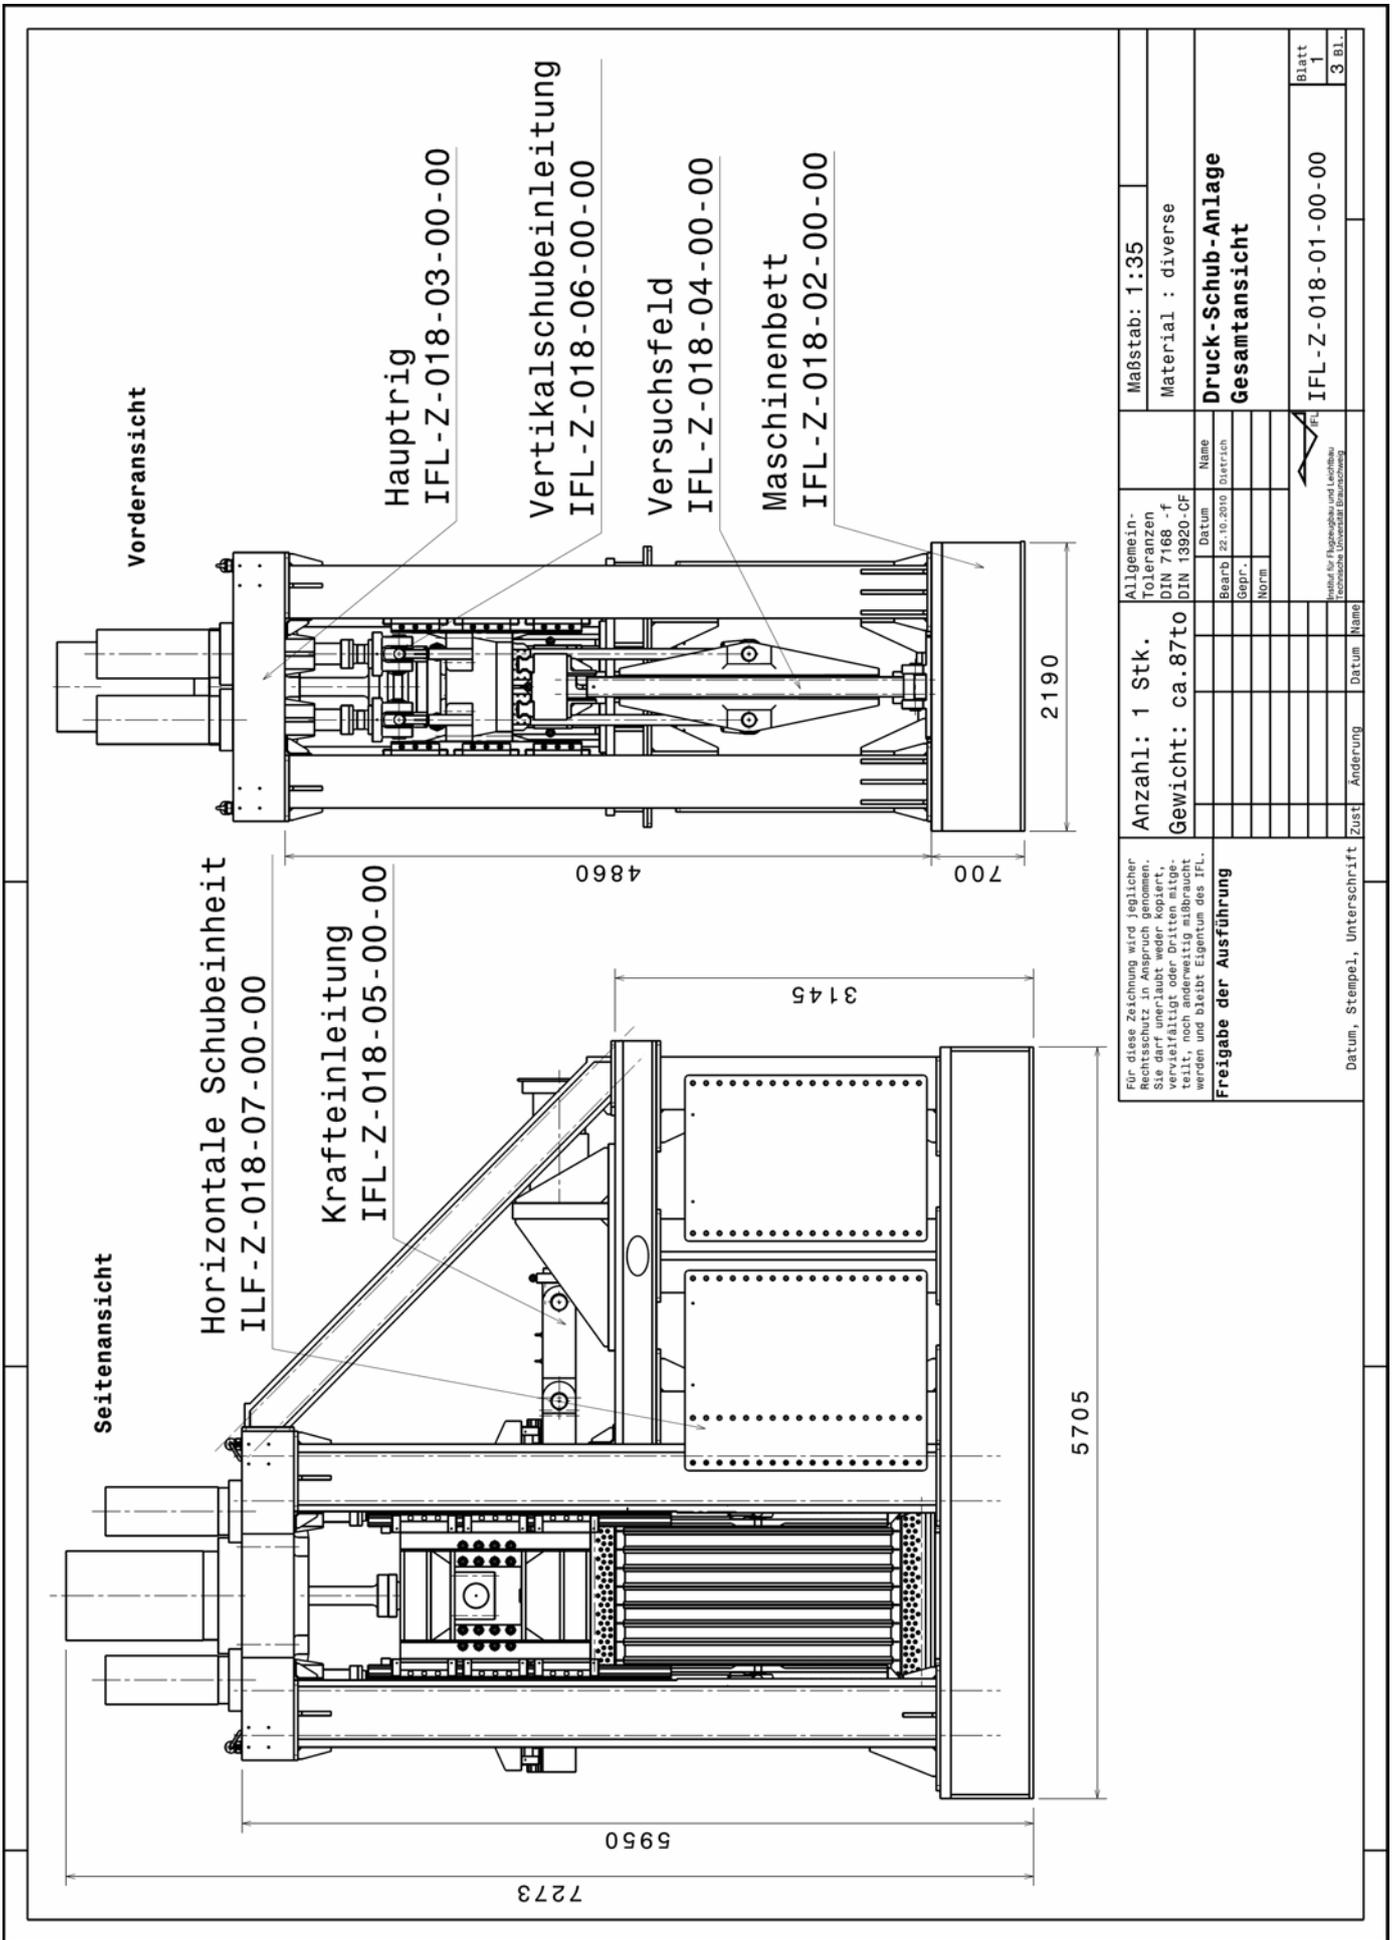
Gesamtansicht der Universalprüfmaschine
